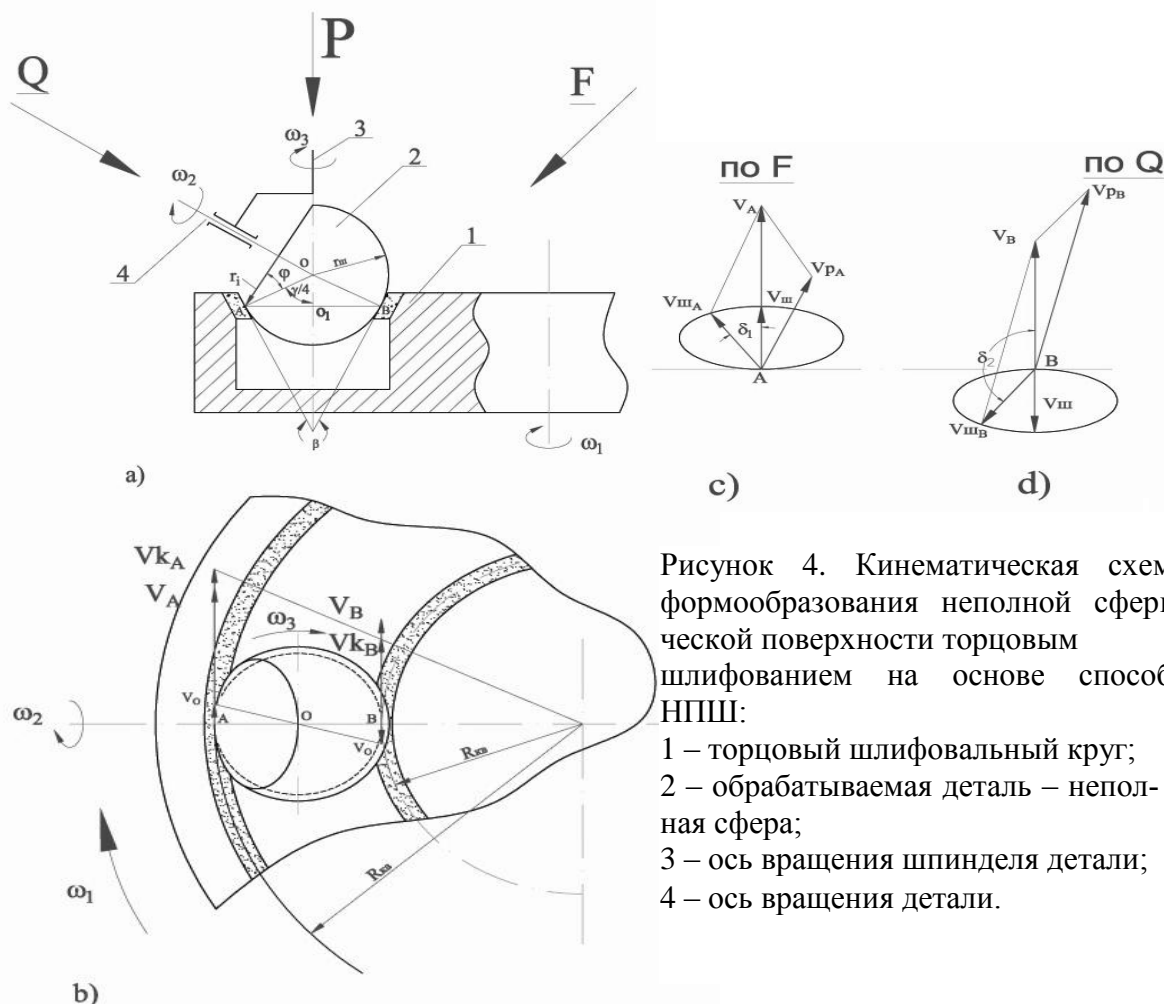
Кинематическая схема формообразования неполной сферической поверхности торцовым шлифованием на основе способа НПШ:
